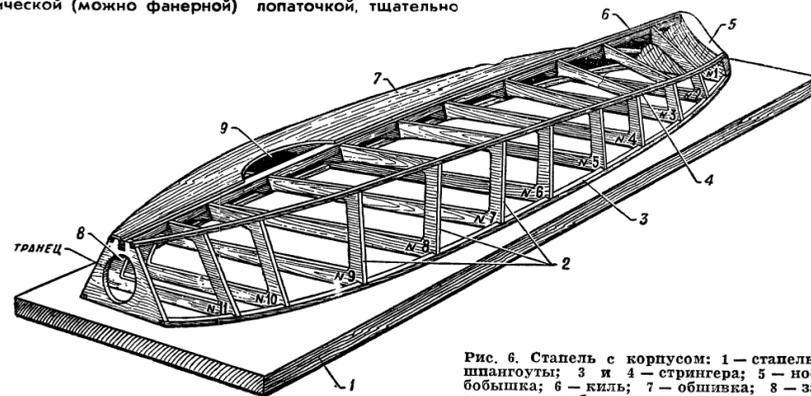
Стапель с корпусом: 1 — стапель; 2 — шпангоуты; 3 и 4 — стрингера; 5 — носовая бобышка; 6 — киль; 7 — обшивка; 8 — заднее отверстие трубы; 9 — входное отверстие трубы
